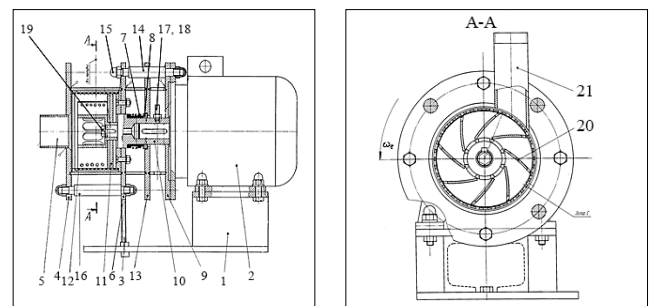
Общая схема дисмембратора: 1 – площадка крепления; 2 – двигатель; 3 – опорная шпилька; 4 – корпус; 5 – всасывающий патрубок; 6, 9 – проставки; 7 – муфта торцевая; 8 – торцевое уплотнение, кольцо керамическое; 10 – вал-втулка; 11 – крыльчатка; 12 – статор; 13 – фланец; 14 – шпилька; 15 – колпачковая гайка; 16 – шпилька; 17 – винт; 18 – контргайка; 19 – болт; 20 – лопасть крыльчатки; 21 – выходной патрубок
